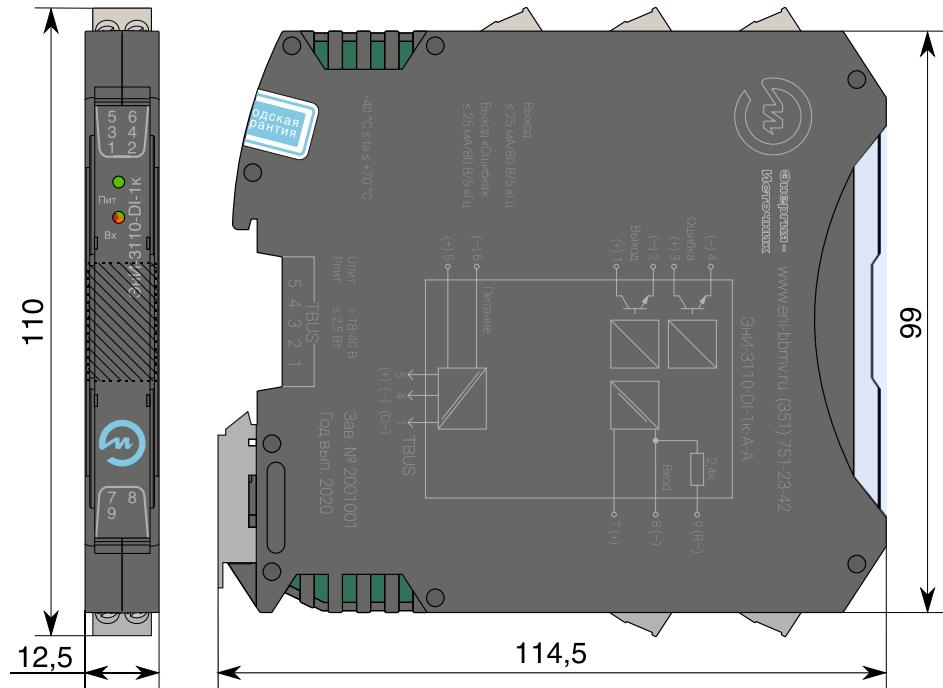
Габаритные размеры модуля с разъемами с винтовыми клеммниками
